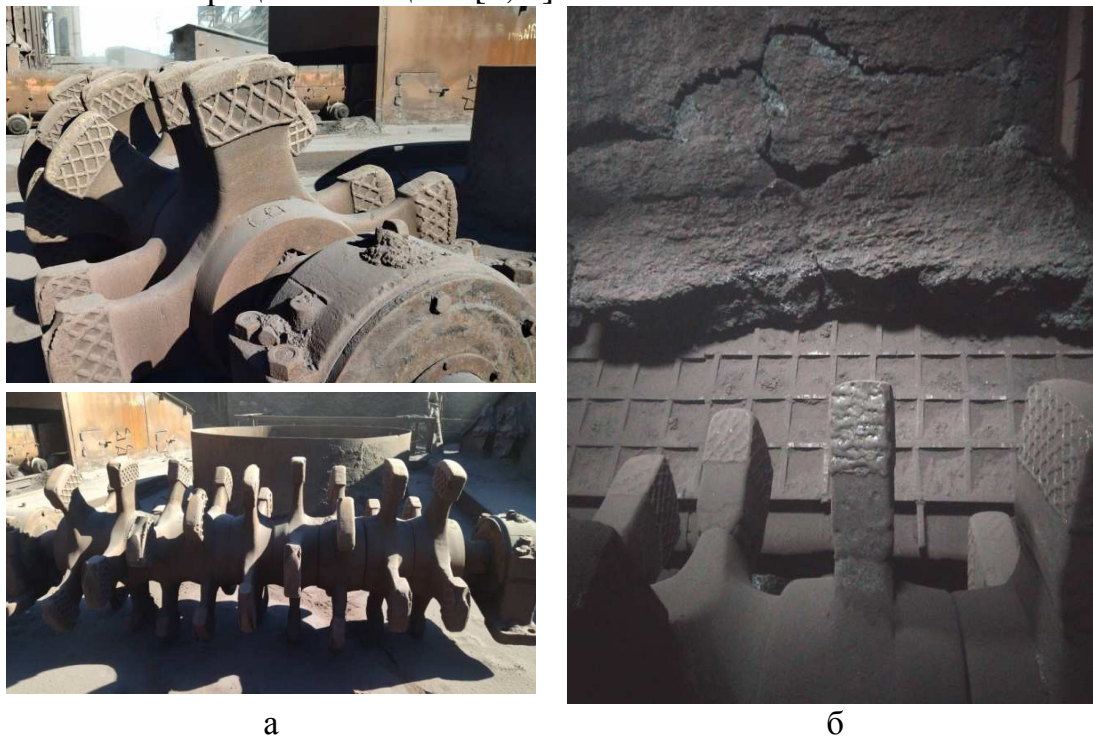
Дробилка ДО-1300-2700-61 усовершенствованной конструкции: ротор с нелинейным расположением зубьев (а) и рабочее пространство (б) дробилки
